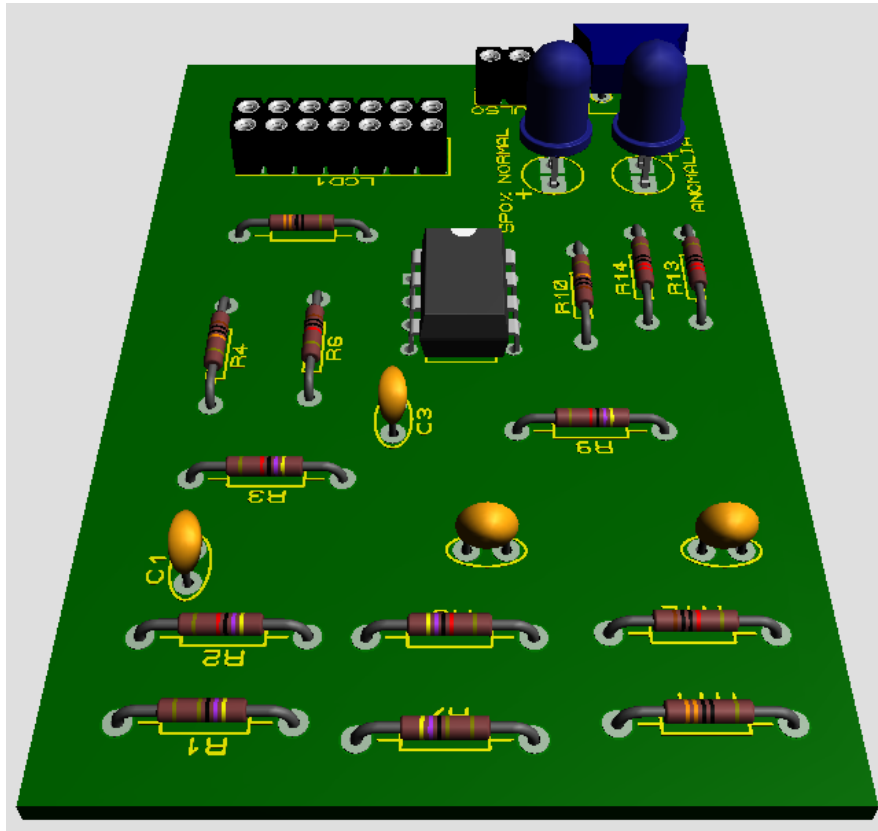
Vista Izquierda de Circuito en Placa PCB
